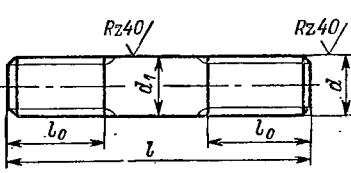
Шпильки повышенной точности для деталей с гладкими отверстиями
